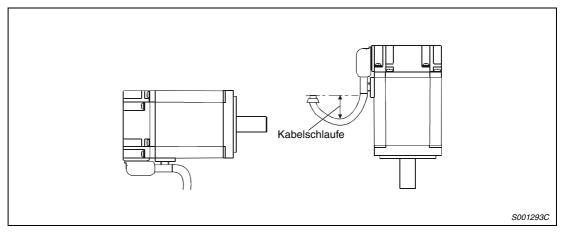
Montage des Servomotors horizontal oder vertikal mit Kabelschlaufe
